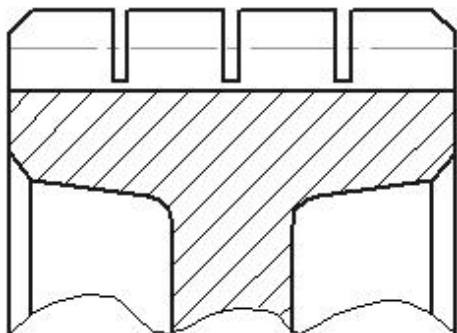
Зубчатый венец с кольцевыми прорезями
